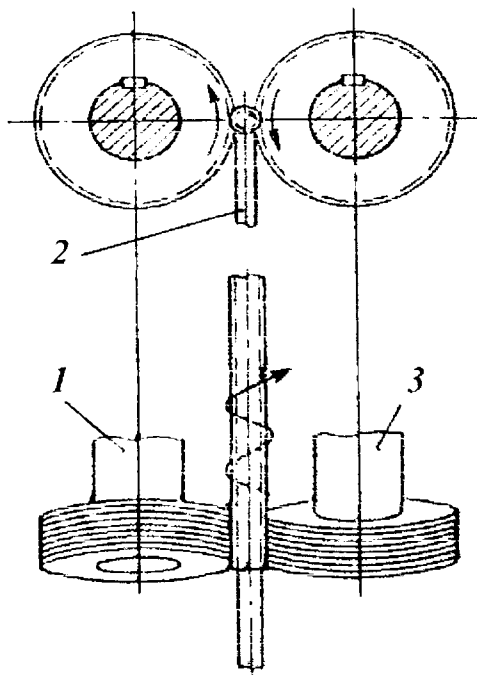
Схема накатывания резьбы с осевой подачей: 1,3 – резьбонакатные ролики, 2 – опора
